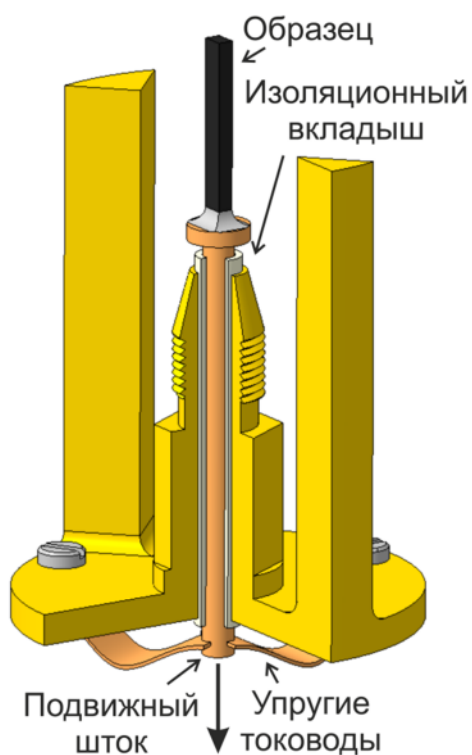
Схема подвижной цанги крепления образца в разрезе
